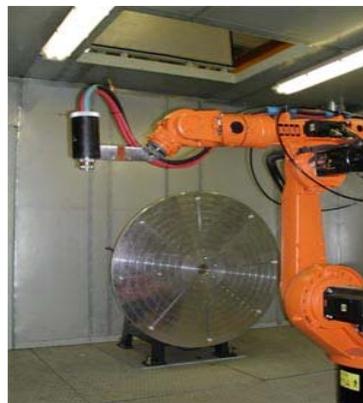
Установка для плазменного напыления ТСЗП-МФ-Р-1000 (плазматрон F4 с манипулятором)
